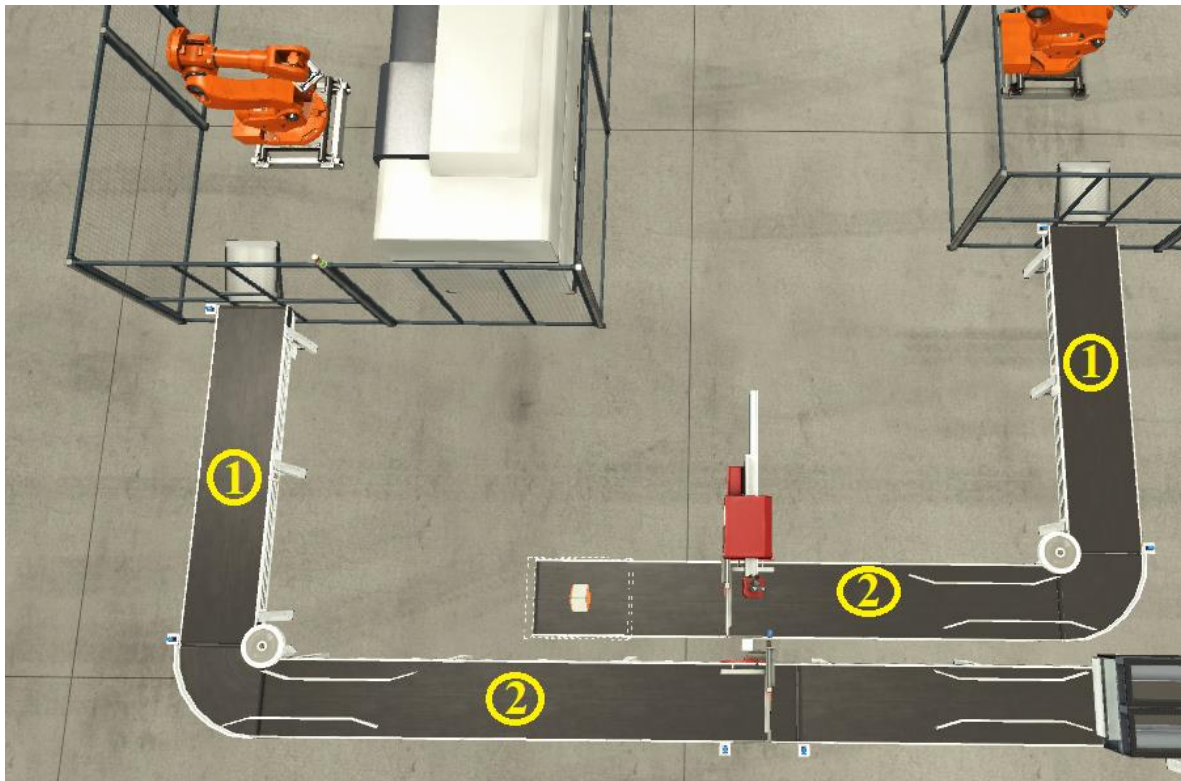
Vista en planta de las cintas de salida de los centros de mecanizado.
